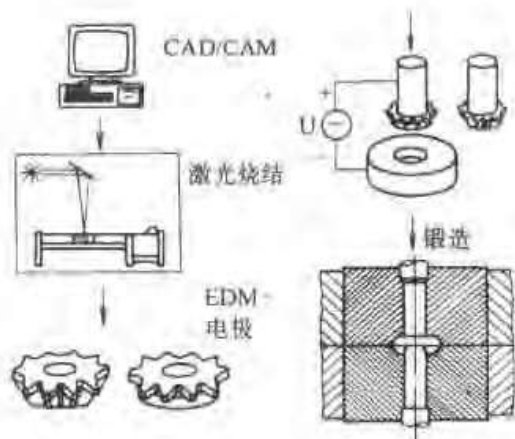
利用 SLS 加工 EDM 电极制造模具
